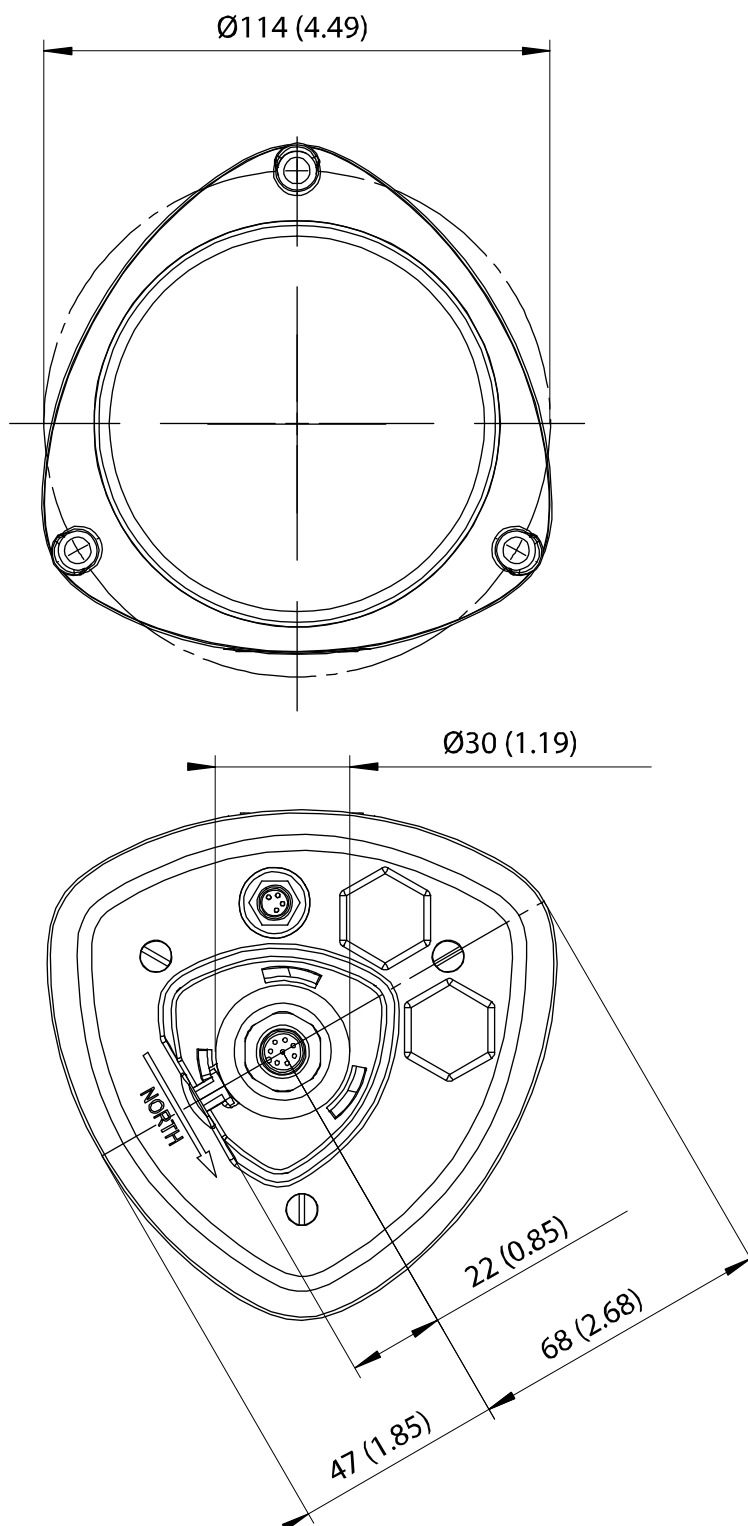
WXT520 Dimensions, vue du sommet et de l'extrémité inférieure
